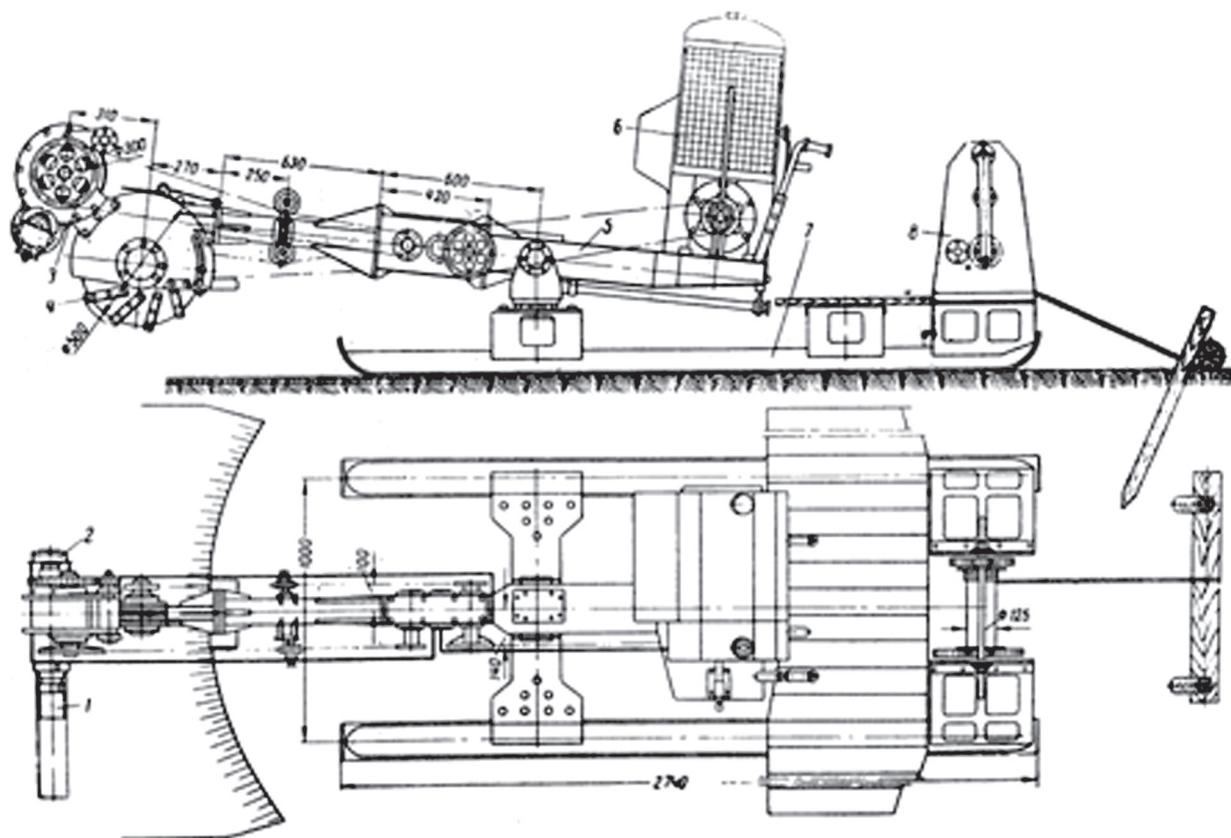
Общий вид машины МПДМ-1: 1 – мундштук; 2 – шнековый пресс; 3 – щелевой пресс; 4 – фреза; 5 – стрела; 6 – двигатель; 7 – лыжи; 8 – лебедка
